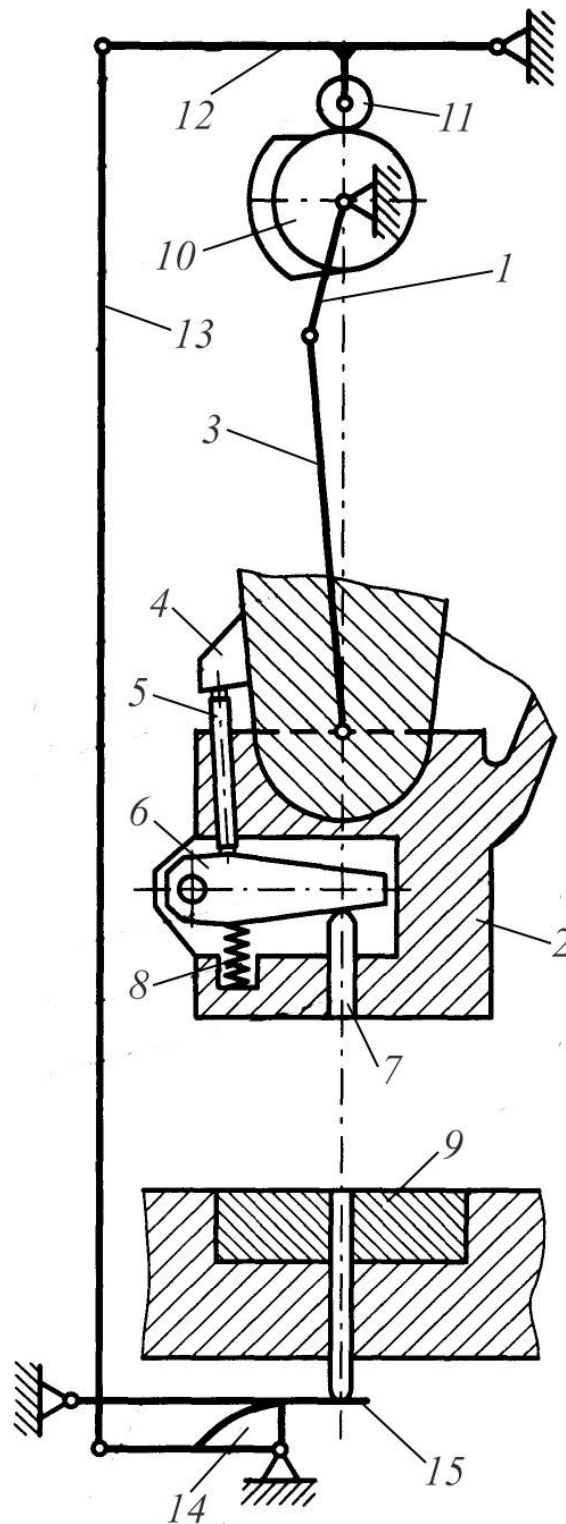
Кинематическая схема прессы с двумя выталкивателями.
